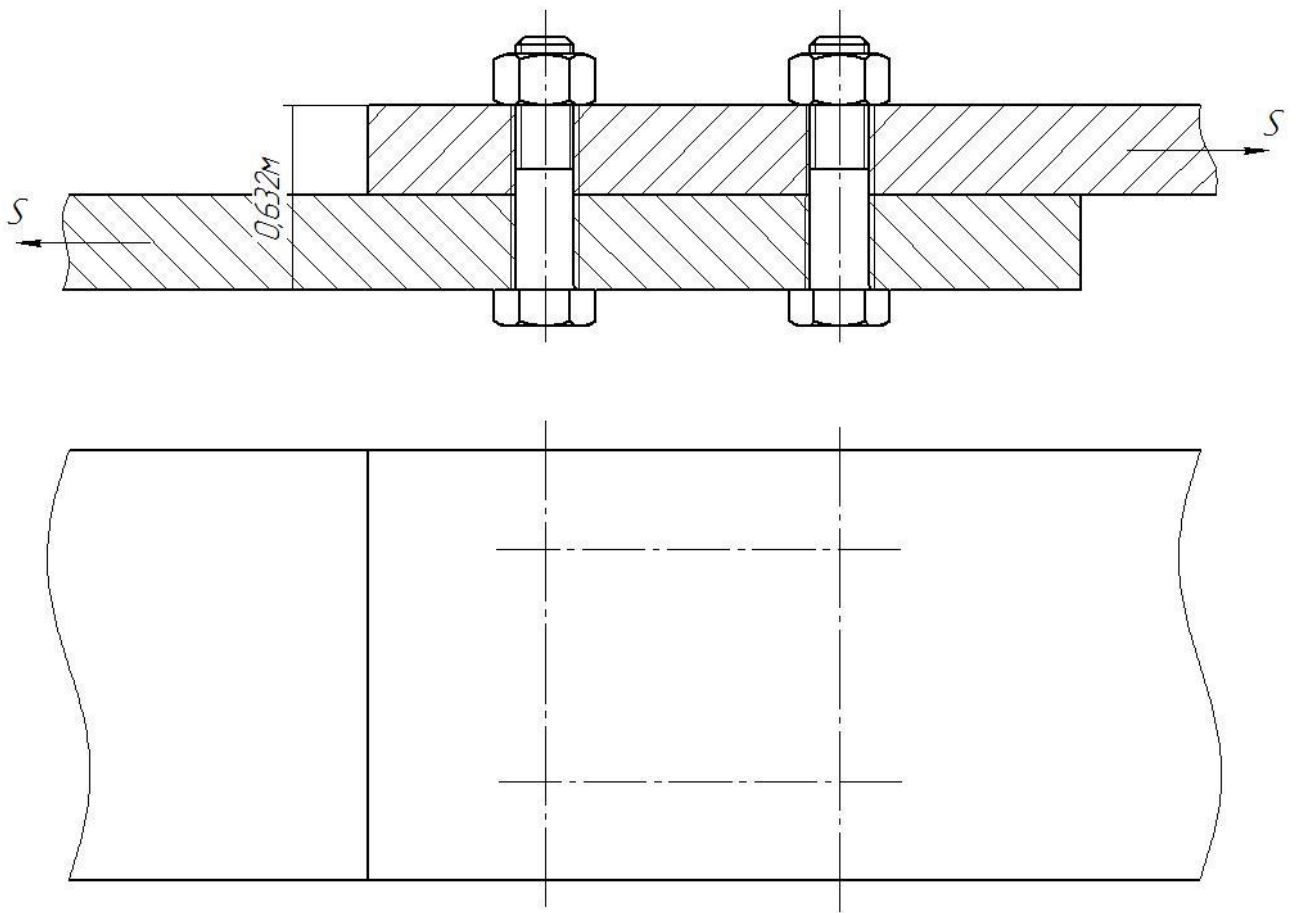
Розрахункова схема різьбового з'єднання при визначенні зусилля затягування
